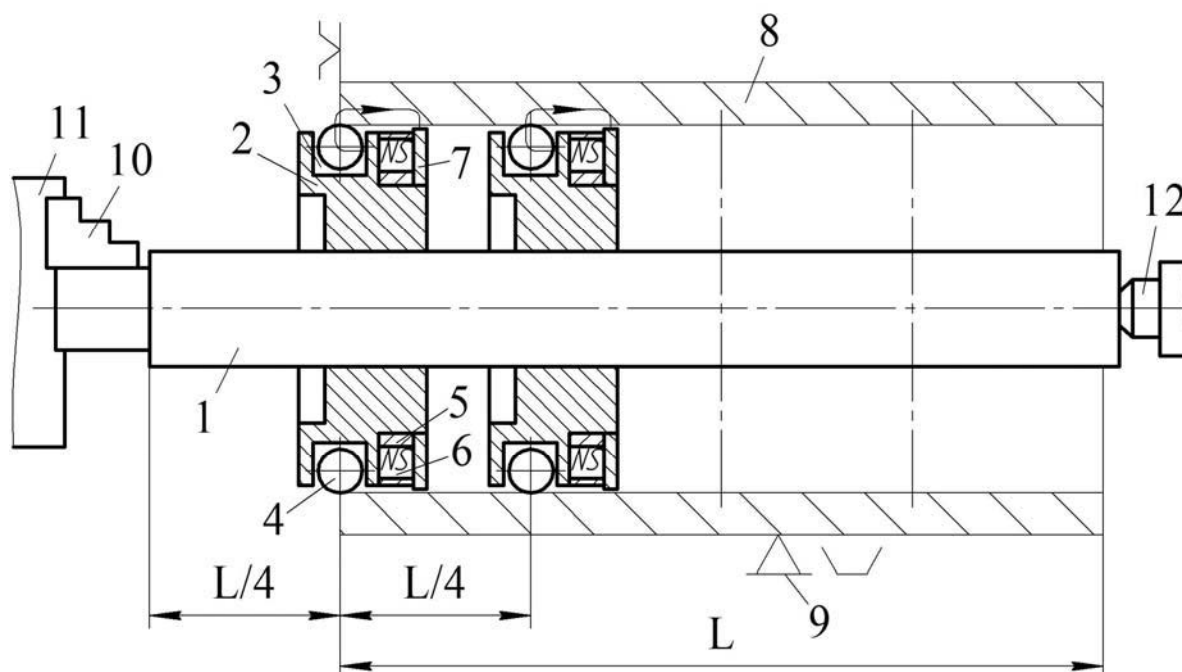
Инструмент для СМДН внутренней поверхности цилиндров большой длины
